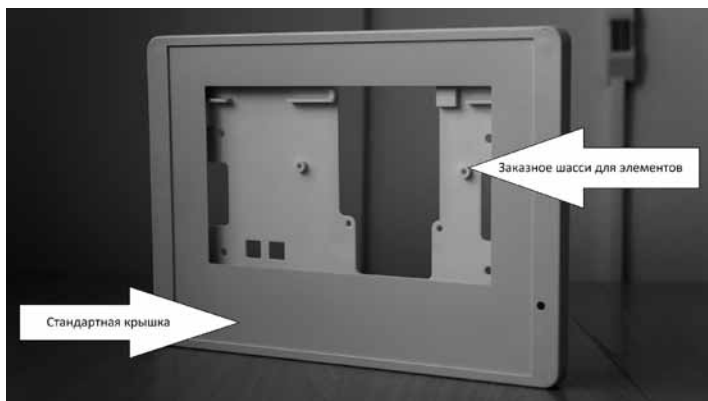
Крышка стандартного пультавого корпуса ОКВ оборудована заказным шасси для размещения навесных элементов. Шасси изготовлено склейкой фрезерованных из листовой пластмассы деталей
